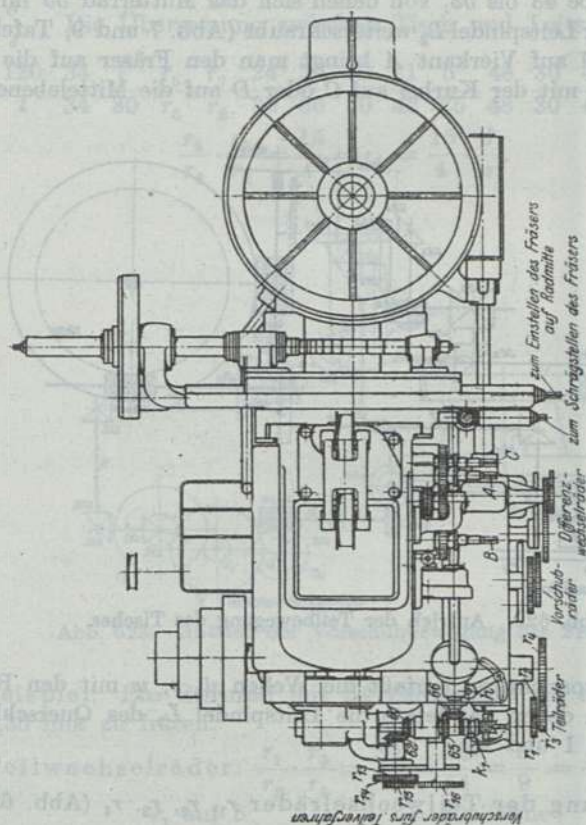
Allgemeine Räderfräsmaschine. J. E. Reinecker, A.-G., Chemnitz.
